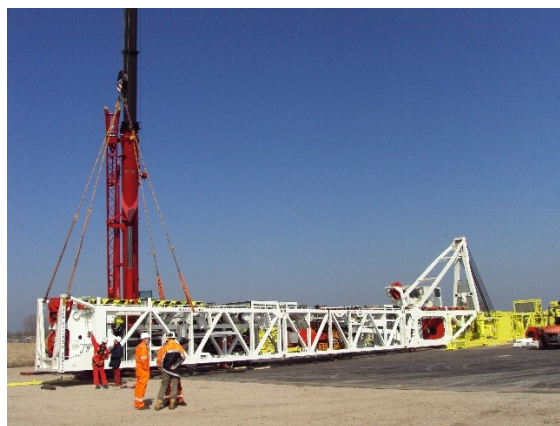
Pohyb mechanismu při zvedání Obr. 2.12 Montáž mechanismu
